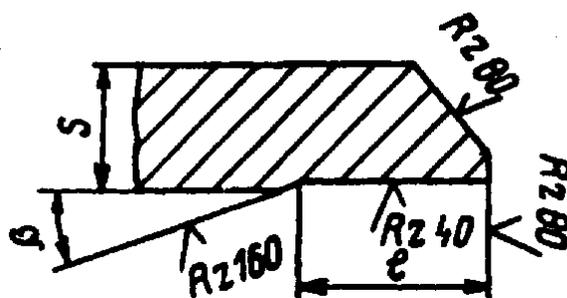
Конструктивные размеры кромки трубы, обработанной под подкладное кольцо
